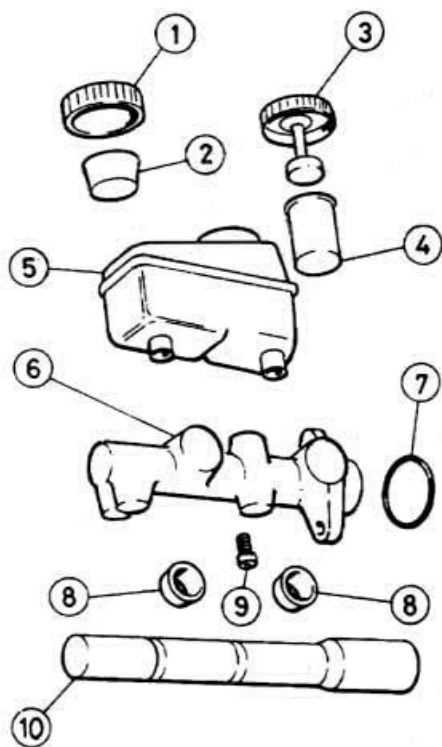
Главный тормозной цилиндр типа АТЕ в разобранном виде:
